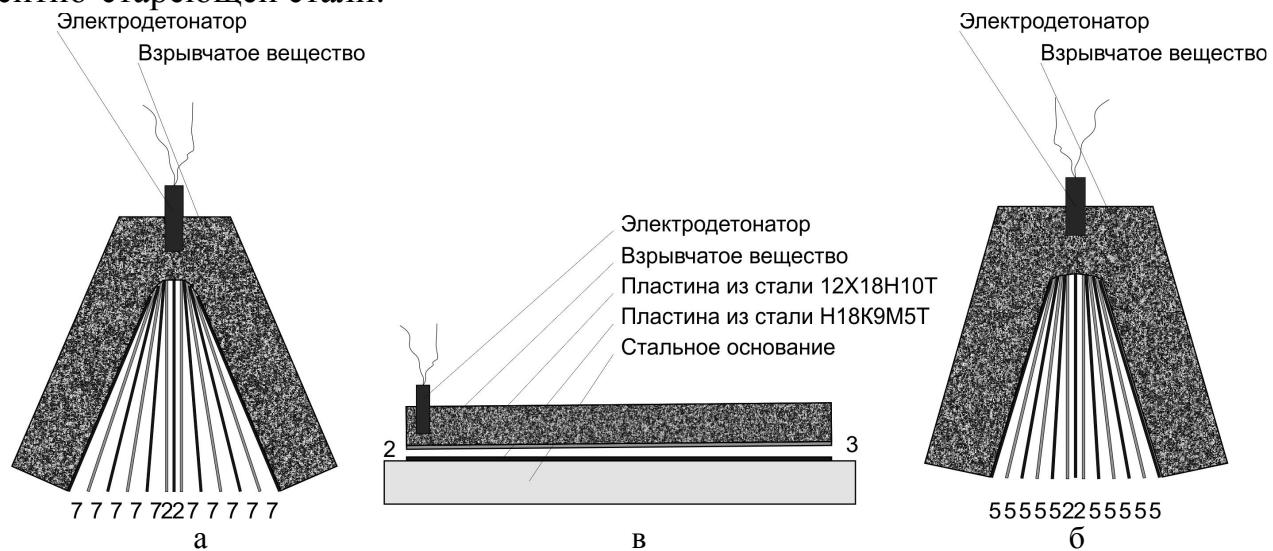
Схемы получения тринадцатислойных композиционных материалов методом сварки взрывом пластин из сталей 20 и H18K9M5T0 (а), сталей H18K9M5T и 12X18H10T (б), и двухслойного материала из сталей H18K9M5T и 12X18H10T (в). Цифрами обозначено расстояние между соединяемыми заготовками в мм
